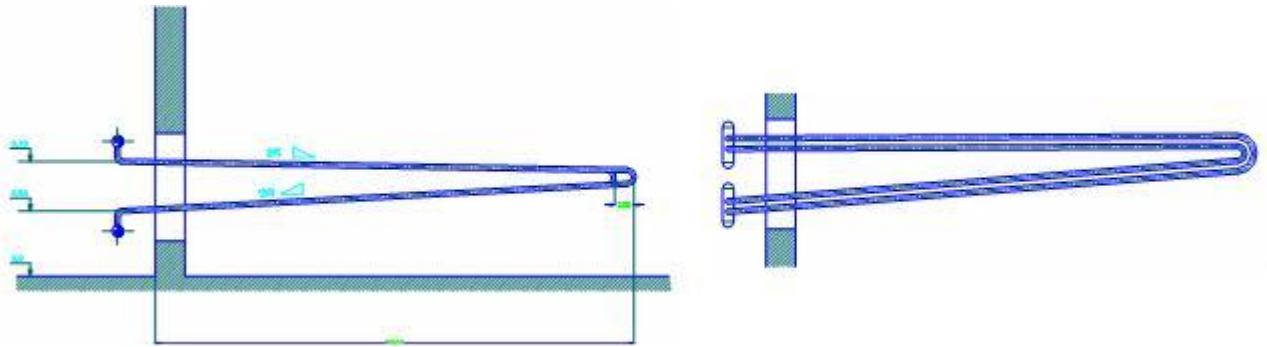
Esquema detallado del Condensador de Aislamiento.
